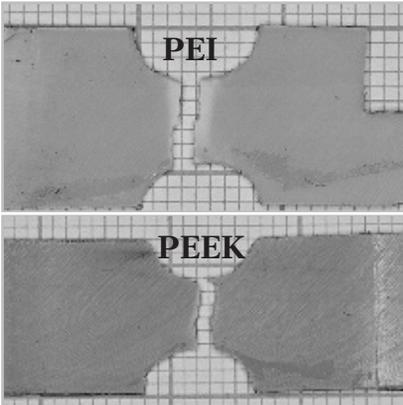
Лопатки, вырезанные из сварных соединений, после механических испытаний
